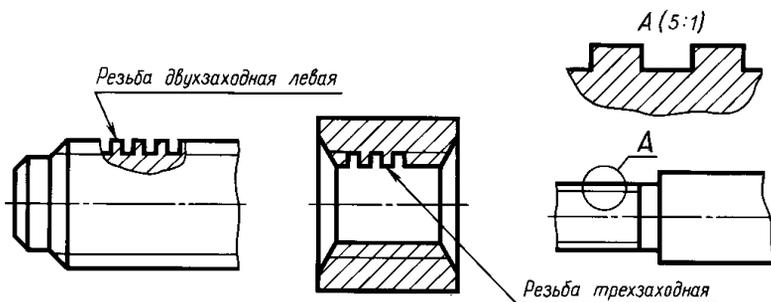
Пример обозначения резьбы с нестандартным профилем
